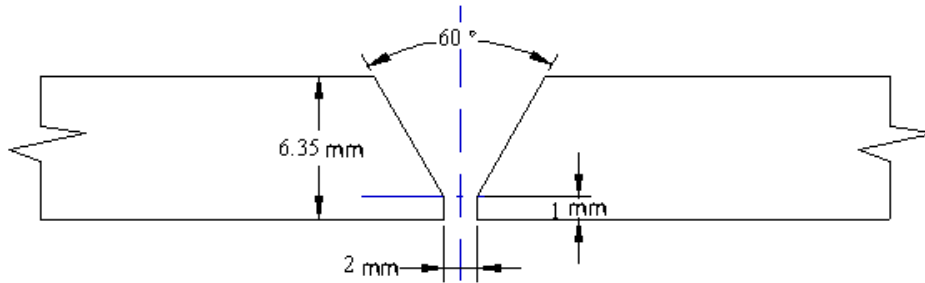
Preparación de la unión utilizada en la realización de los cordones de soldadura
